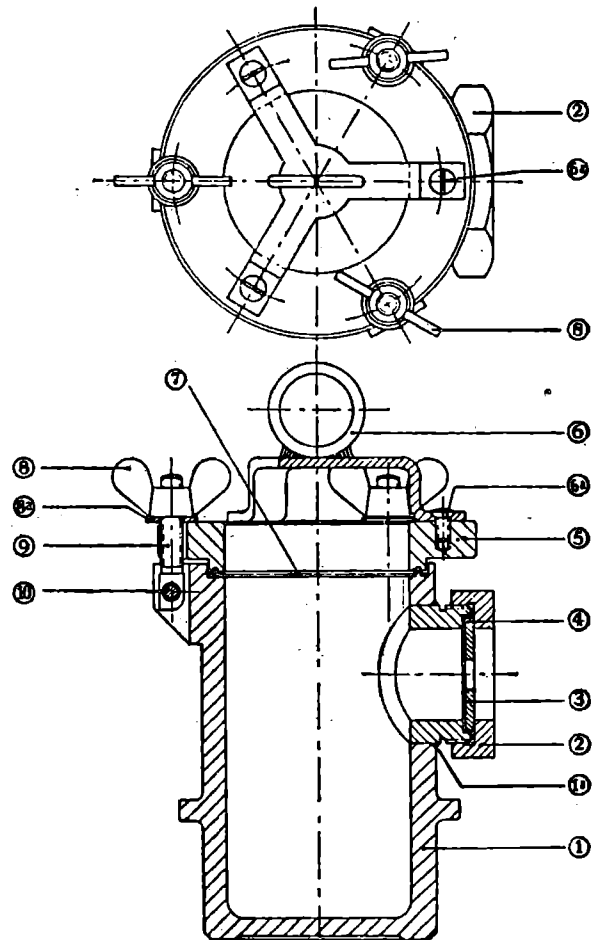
Recipiente a presión montado; vistas esquemáticas en sección vertical y en planta.
